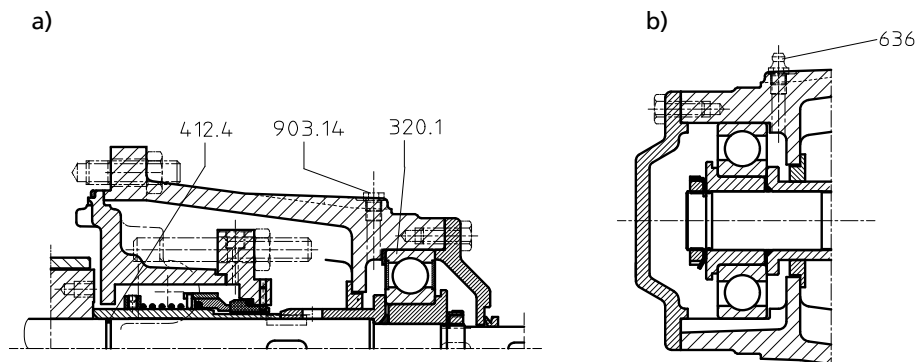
а) Подшипник со стороны привода Multitec 32 - б) Смазка консистентной смазкой через смазочный ниппель с противоположной приводе стороны, типоразмеры 100-150
